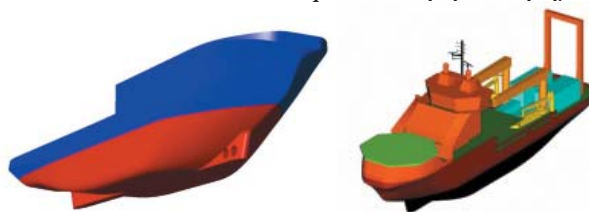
Трехмерная модель формы корпуса (вид с носа)
